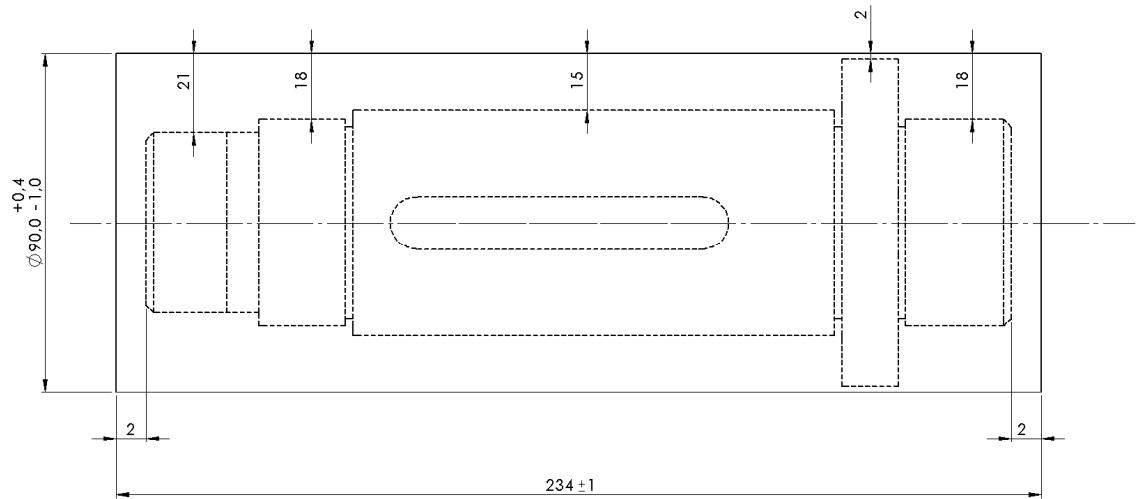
Ескіз з заготовки сортового прокату
